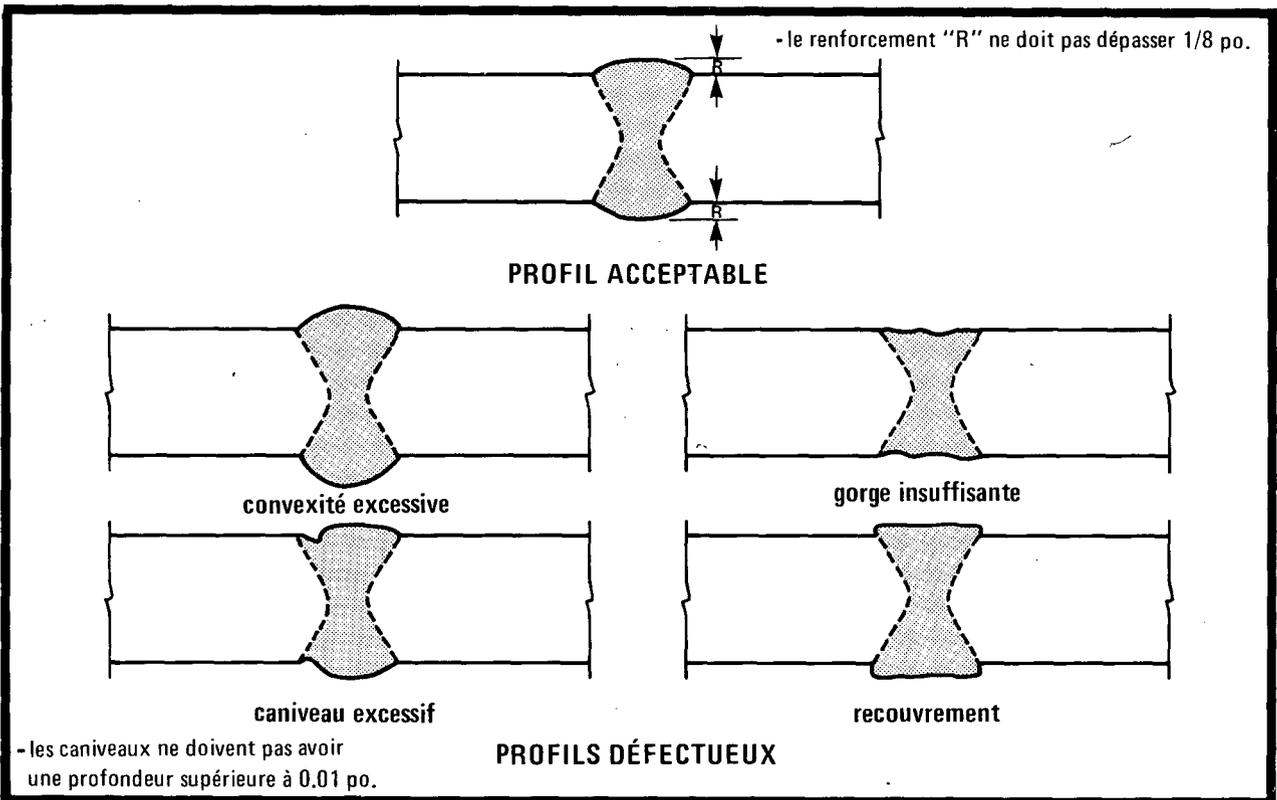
SOUDURE BOUT À BOUT
